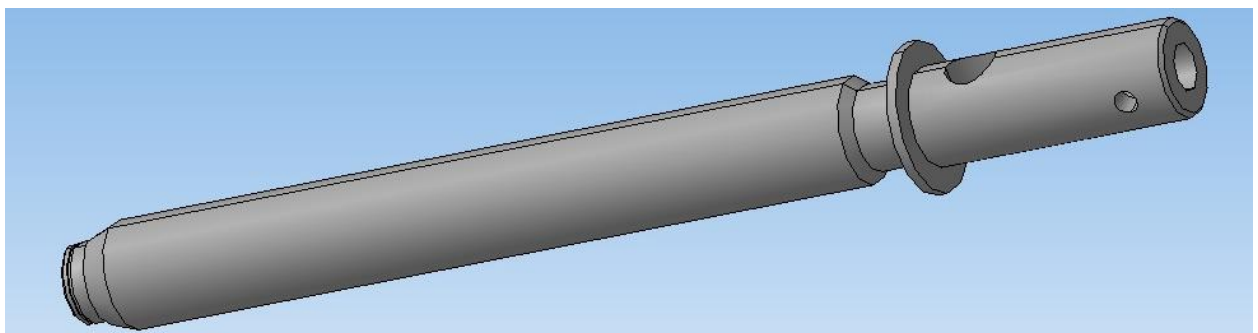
3D-модель деталі «Гвинт БРД 210124»
